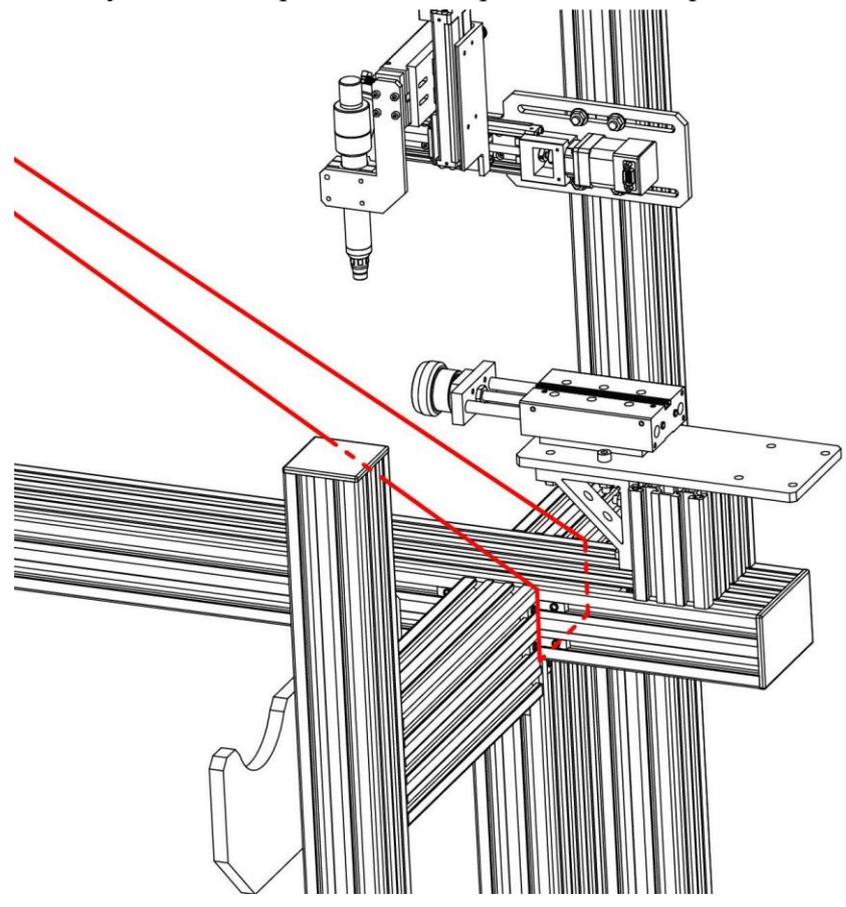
Строповка со стороны правой сварочной головки
